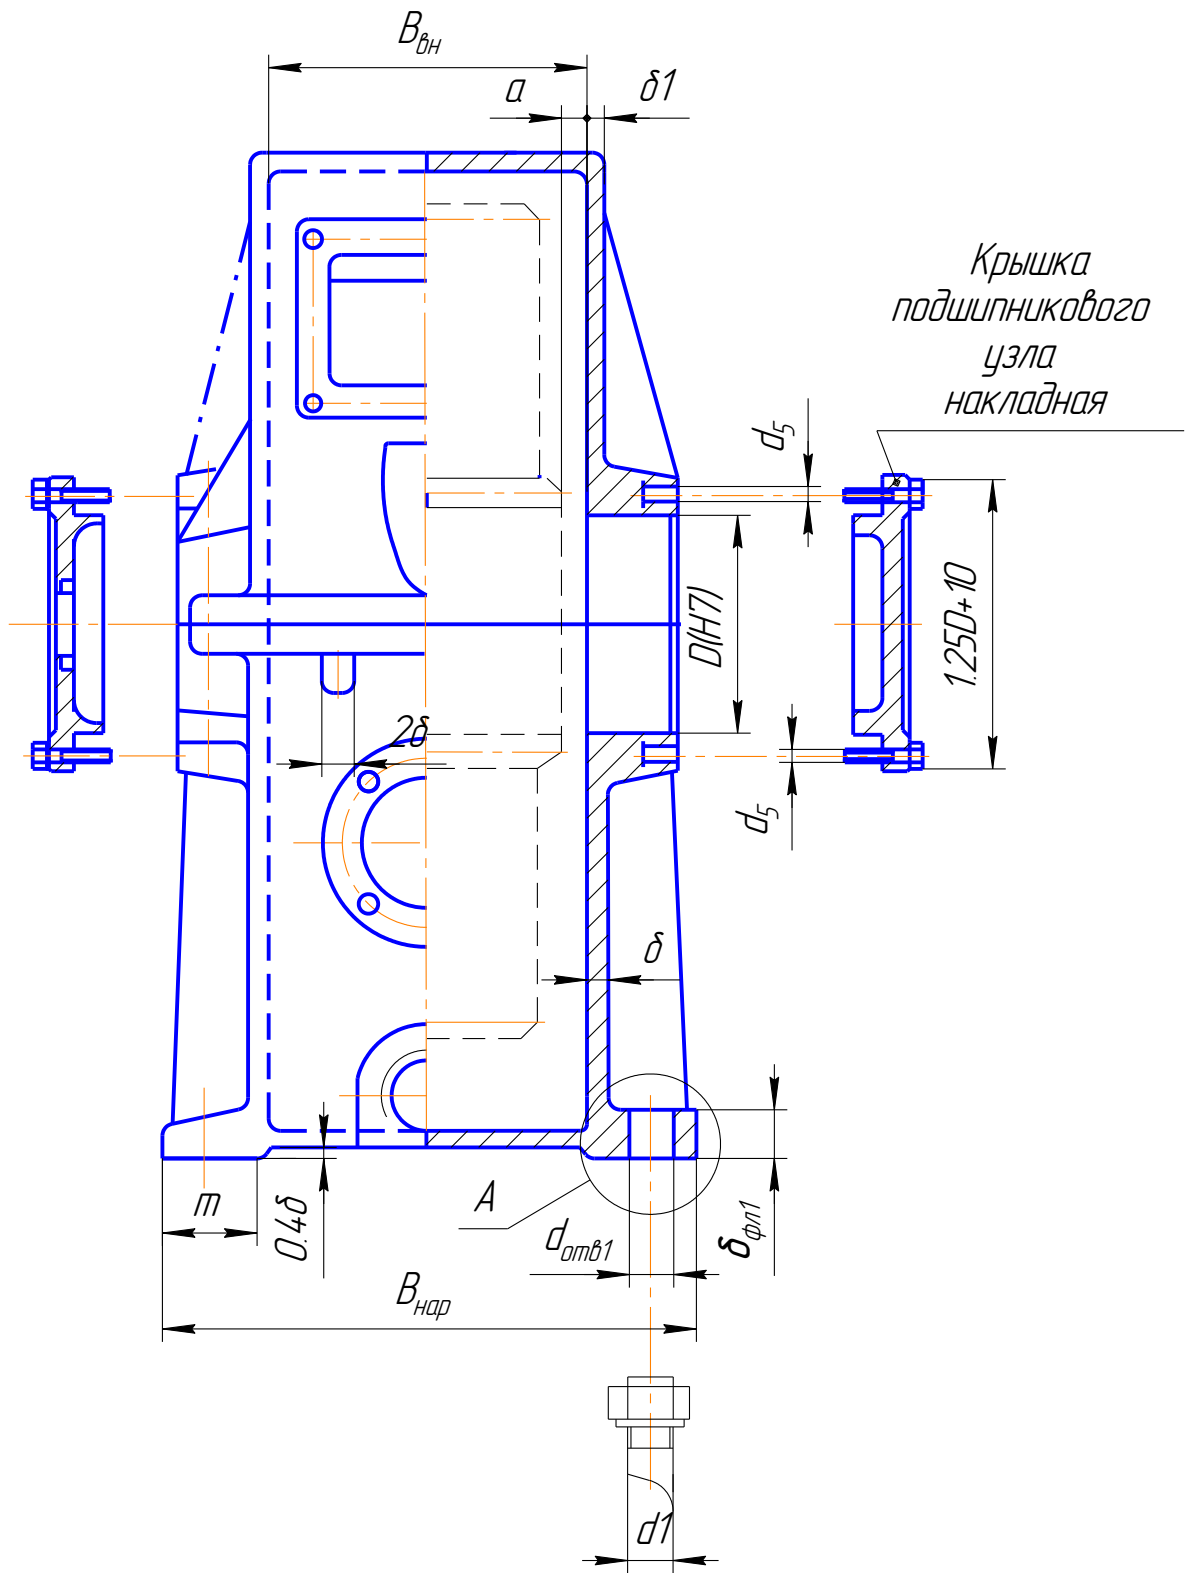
(лист 2, листов 3) Конструкции корпусных деталей цилиндрических редукторов с наружным расположением подшипниковых бобышек
